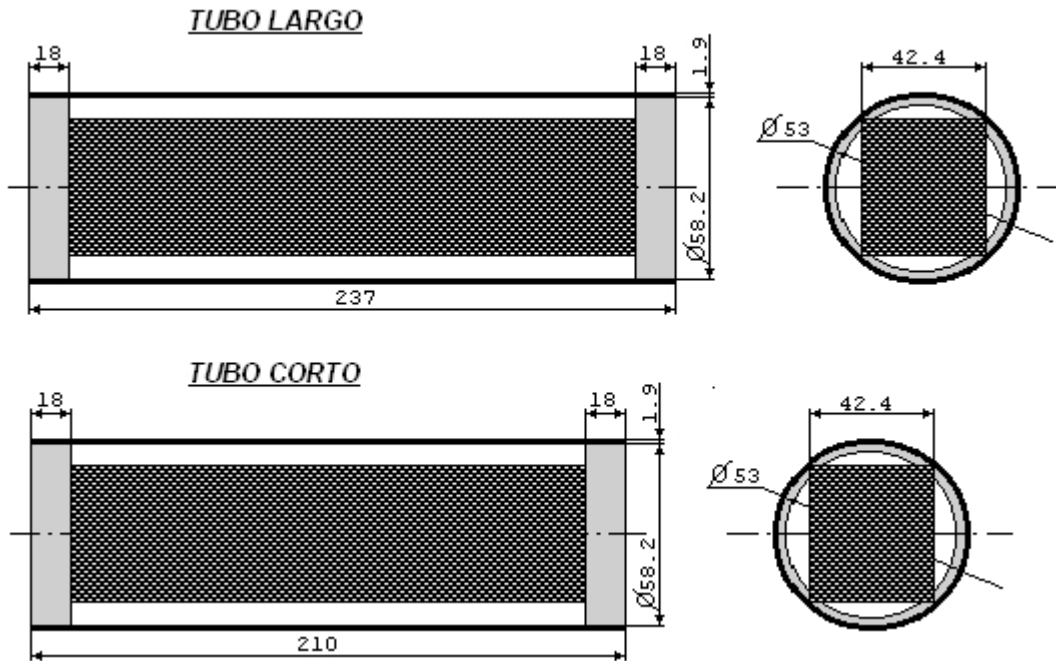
Dimensiones útiles de los tubos (en mm).
